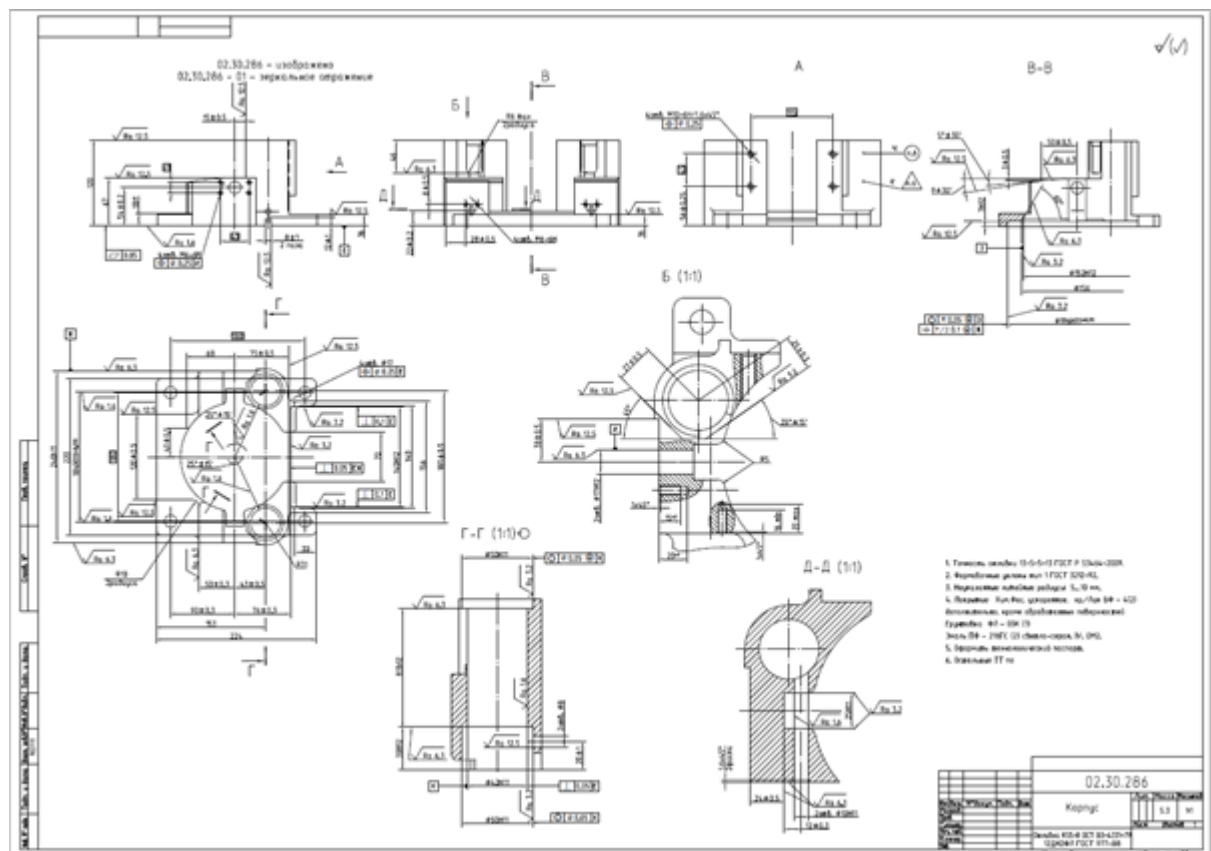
Технический многовидовый чертёж детали 3 «Корпус»
